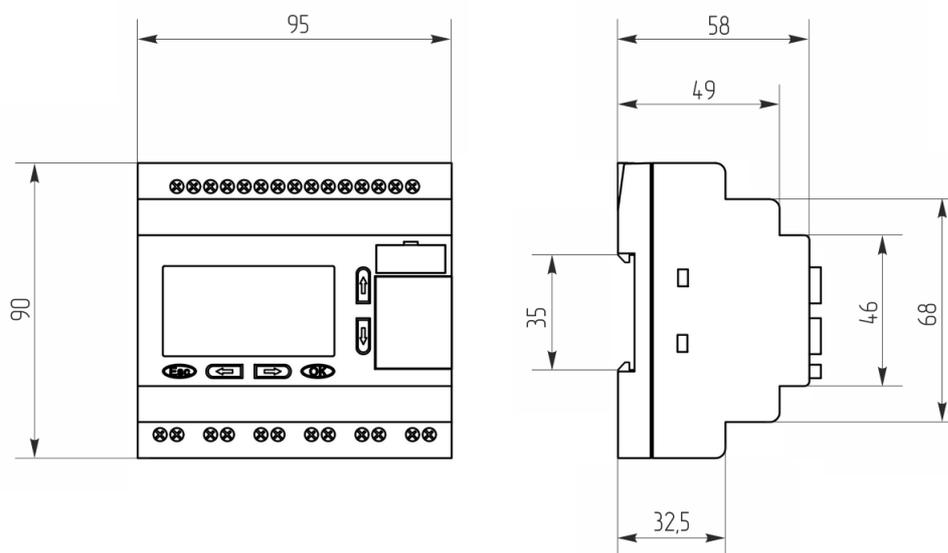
Габаритные и установочные размеры модуля ЦПУ
